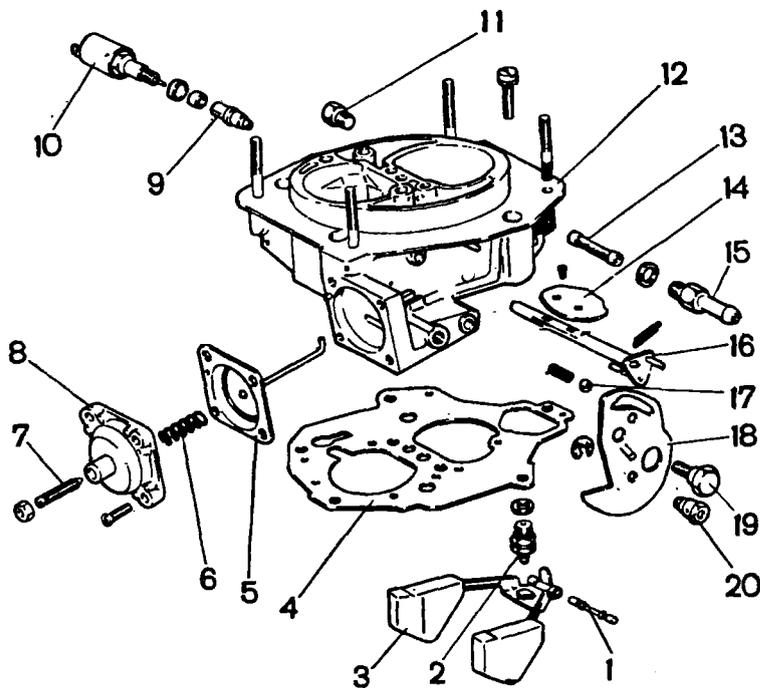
Детали крышки карбюратора 21053-1107010: 1 - ось поплавка; 2 - игольчатый клапан; 3 - поплавок; 4 - прокладка; 5 - диафрагма пускового устройства со штоком; 6 - пружина; 7 - регулировочный винт; 8 - крышка пускового устройства; 9 - топливный жиклер холостого хода; 10 - электромагнитный запорный клапан; 11 - пробка; 12 - крышка карбюратора; 13 - топливный фильтр; 14 - воздушная заслонка; 15 - патрубок подачи топлива; 16 - ось воздушной заслонки с рычагом; 17 - шарик фиксации рычага управления воздушной заслонкой; 18 - рычаг управления воздушной заслонкой; 19 - ось рычага; 20 - втулка крепления тяги привода воздушной заслонки
